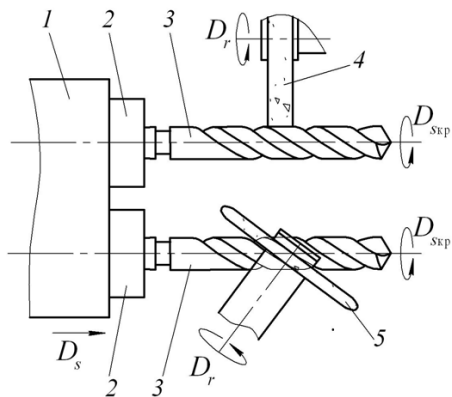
Параллельная схема вышлифовывания канавок и спинок сверла на многопозиционном станке: 1 – револьверная головка; 2 – цанговый патрон; 3 – заготовка; 4 – спиночный круг; 5 – канавочный круг
